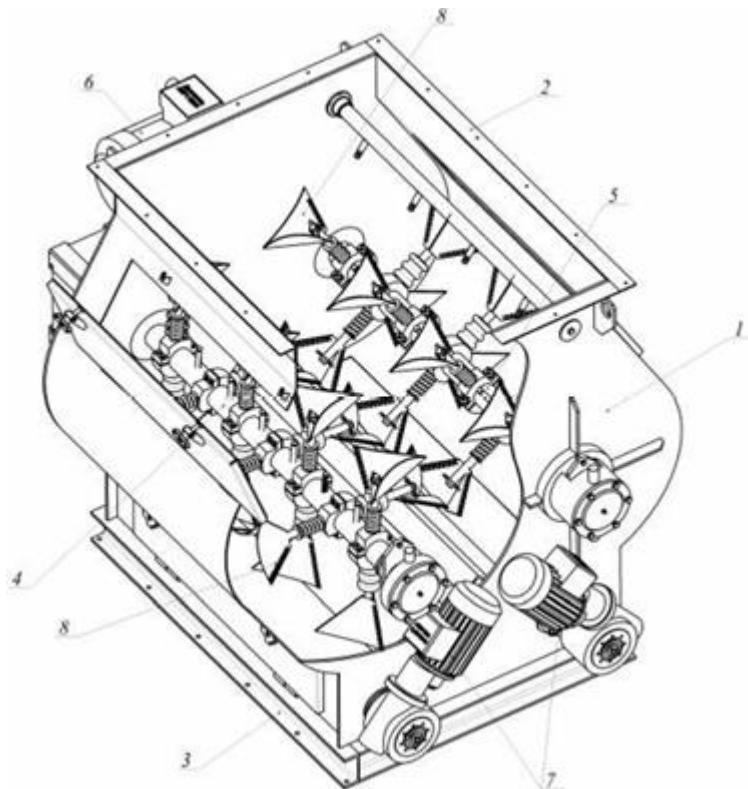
Загальний вигляд двовального лопатевого змішувача
